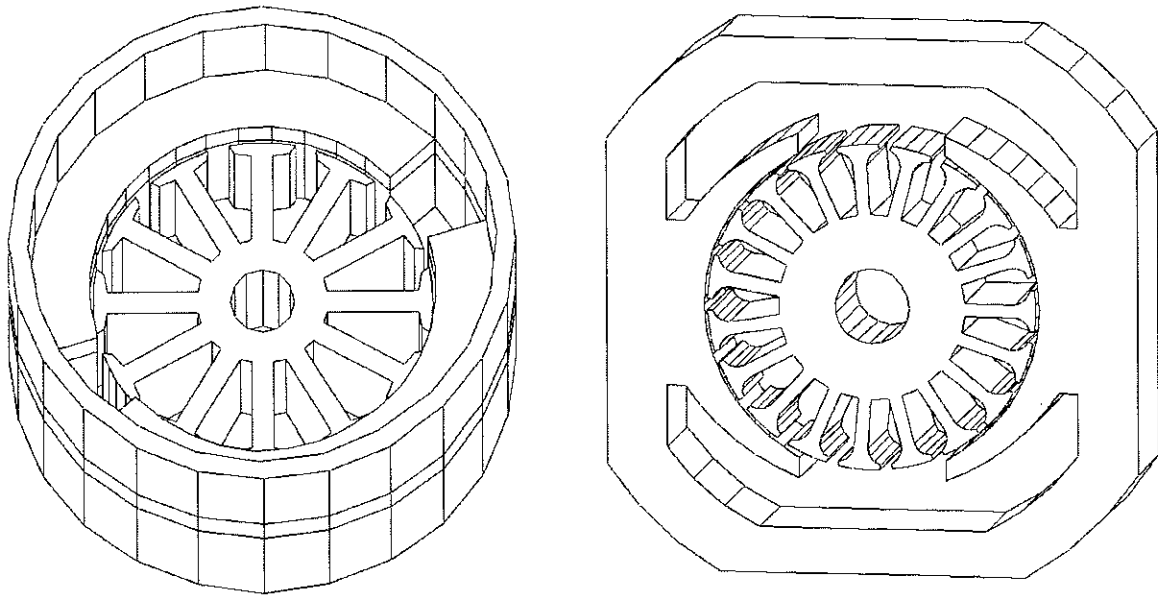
Géométries d'un moteur à aimants et d'une machine universelle
